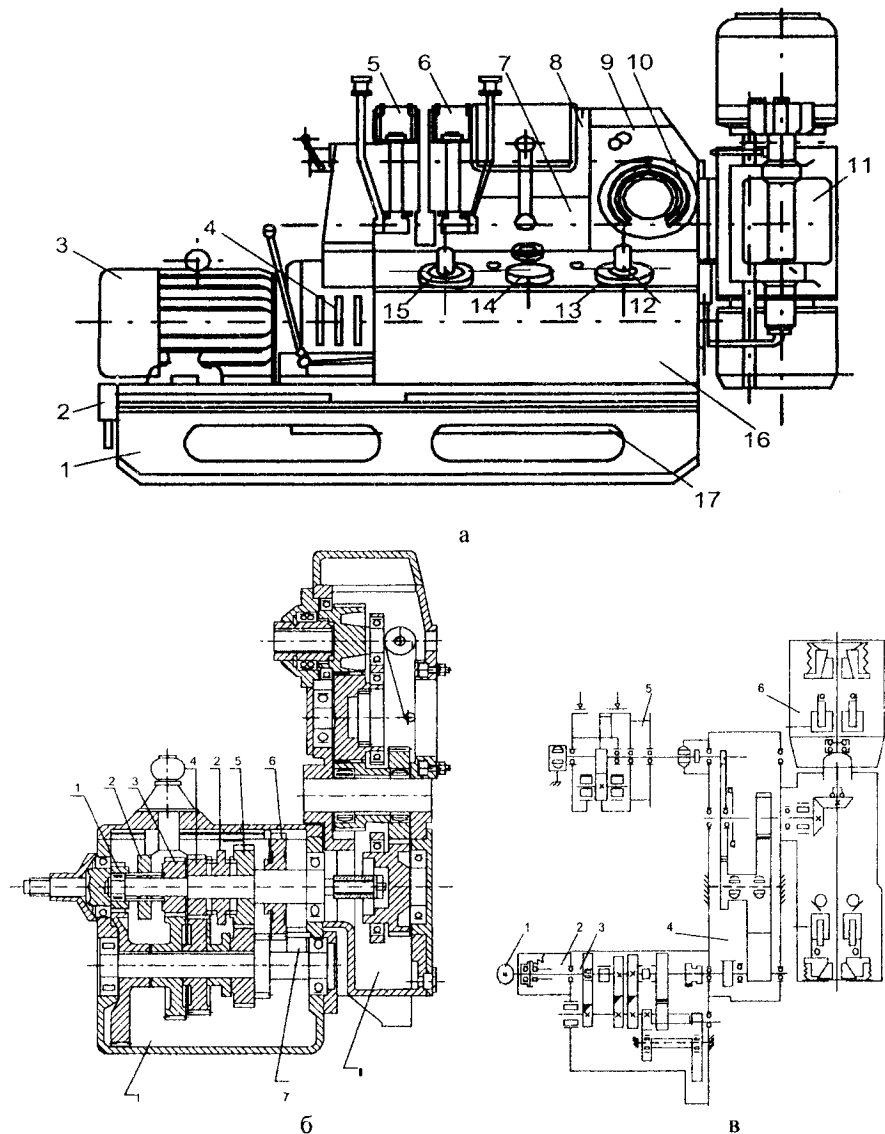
Буровий верстат СКБ-4: а – загальний вигляд; б – трансмісія верстата; в – кінематична схема; 1 – двигун; 2 – фрикціон; 3 – коробка зміни передач; 4 – роздавальна коробка; 5 – лебідка; 6 – затискний патрон
